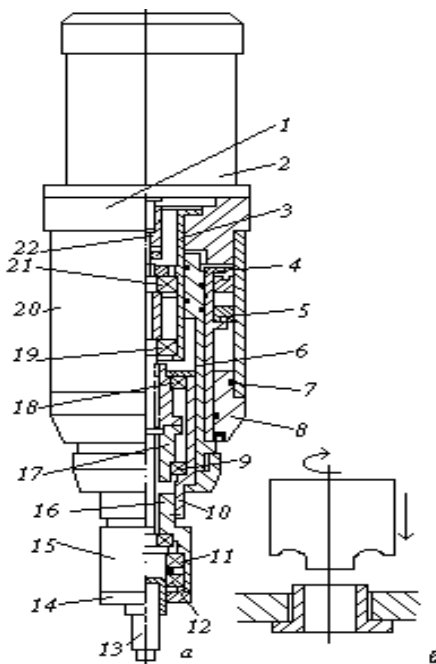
Конструкция одношпindelной вальцовочной головки
